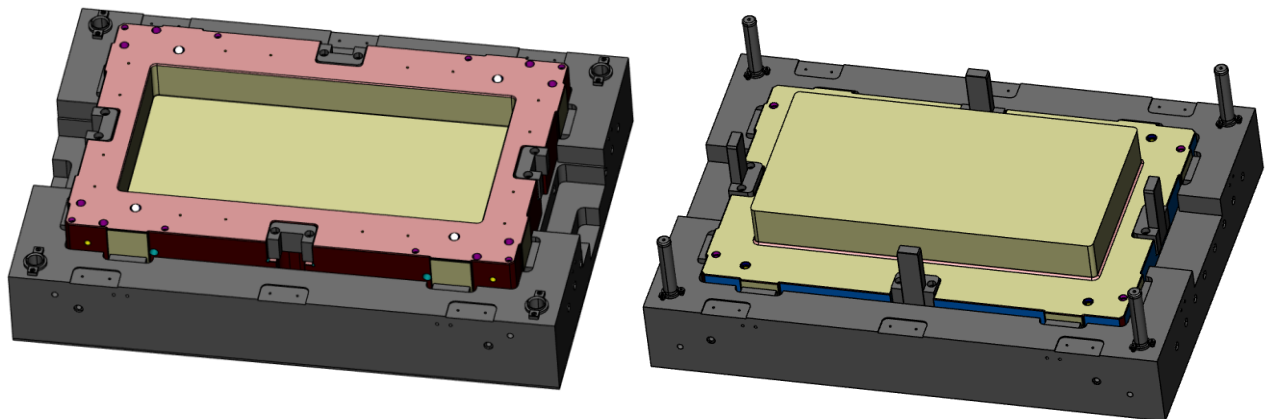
Werkzeughälften zum Pressen verschiedener Plattendicken
